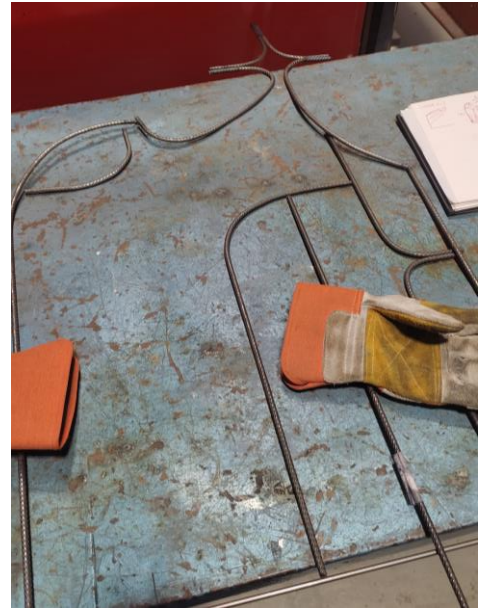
Sara González: proceso de soldadura avanzado.
